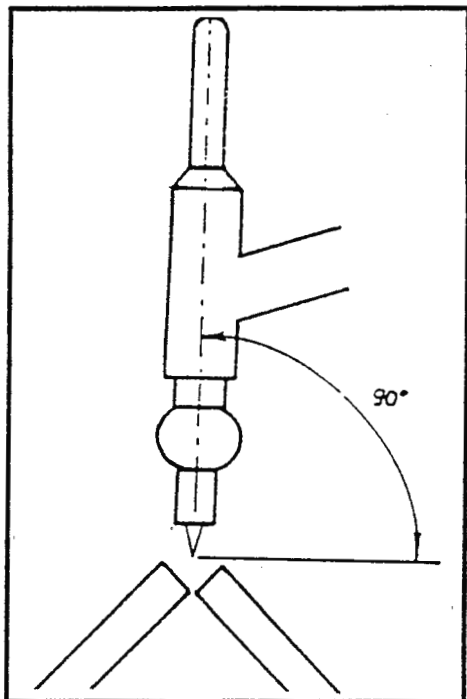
Posición de la pistola en relación a las piezas a soldar visto de lado
